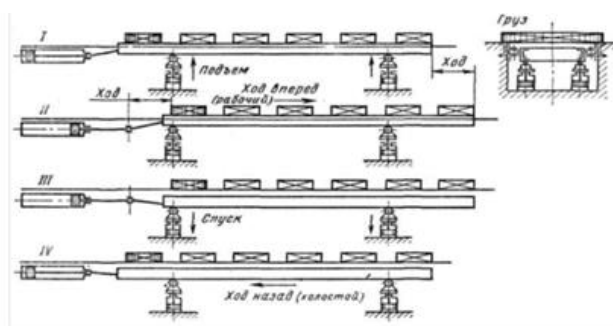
Тяговый транспортёр, приводимый в движение пневмоцилиндром
